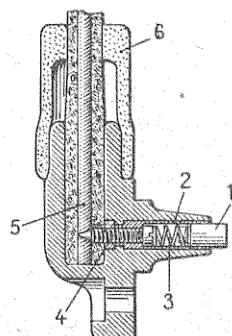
Borne de prise de courant à haute tension de la magnéto de la figure 60.
